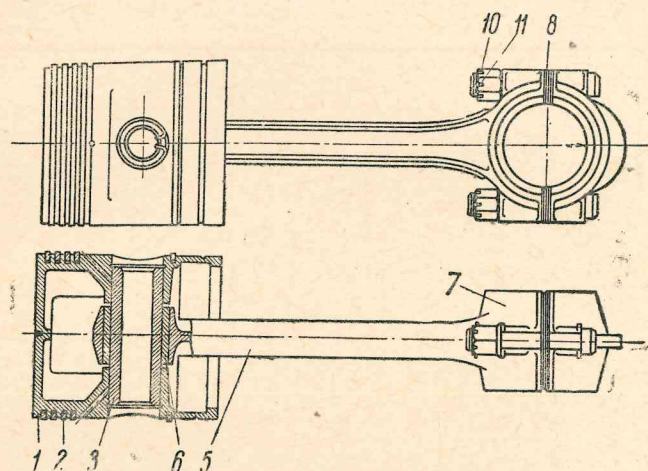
Поршень и шатун двигателя „Сталинец-60“ ЧТЗ
